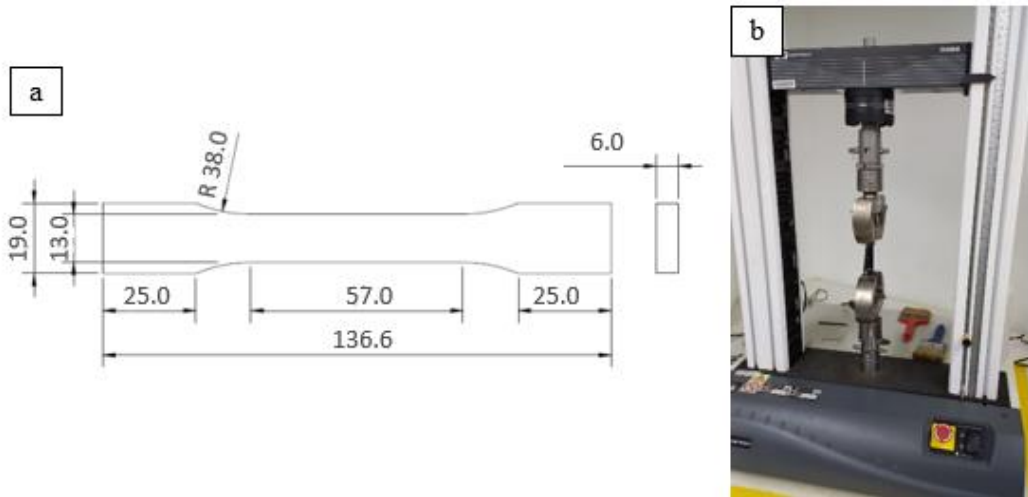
Ensayo a tensión. a) Dimensiones para probeta, las medidas están en mm con tolerancia de $\pm 0.2\text{mm}$, b) Ensayo
